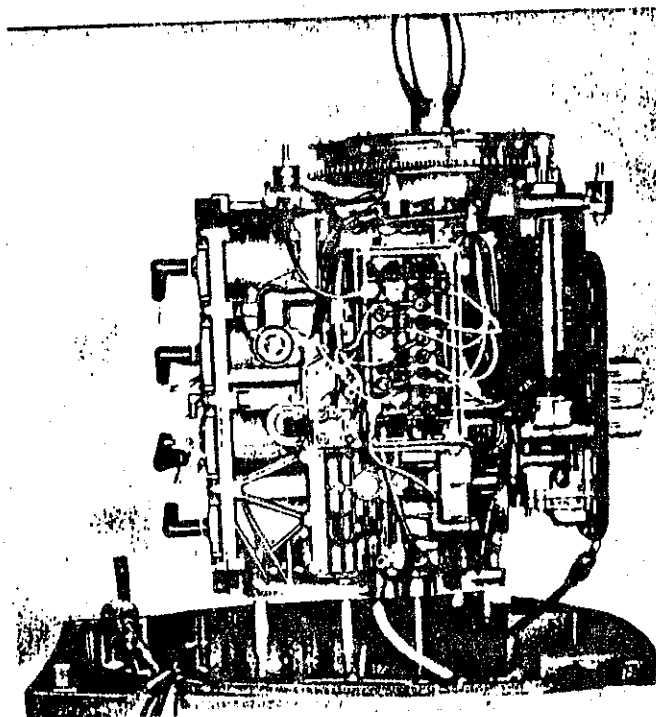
Cabeza motriz, motor de 4 cilindros.
